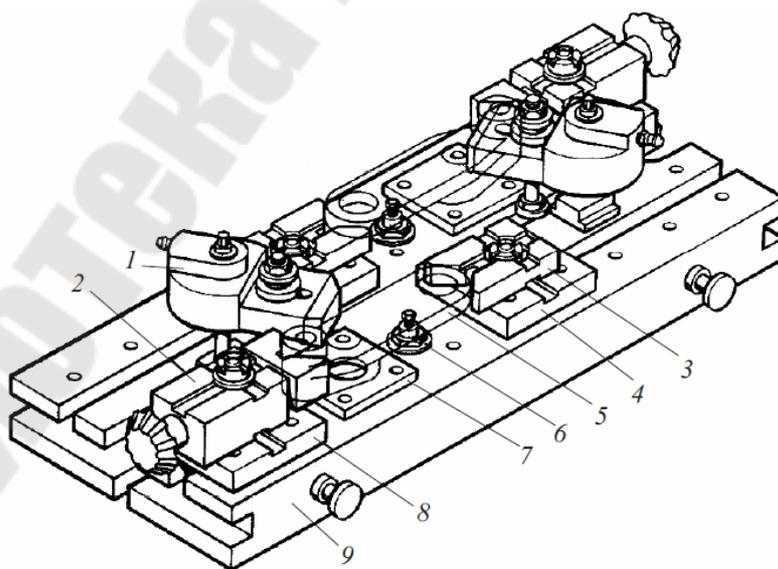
Компоновка приспособления из элементов сборно-разборного приспособления и универсально-сборного приспособления [4]
